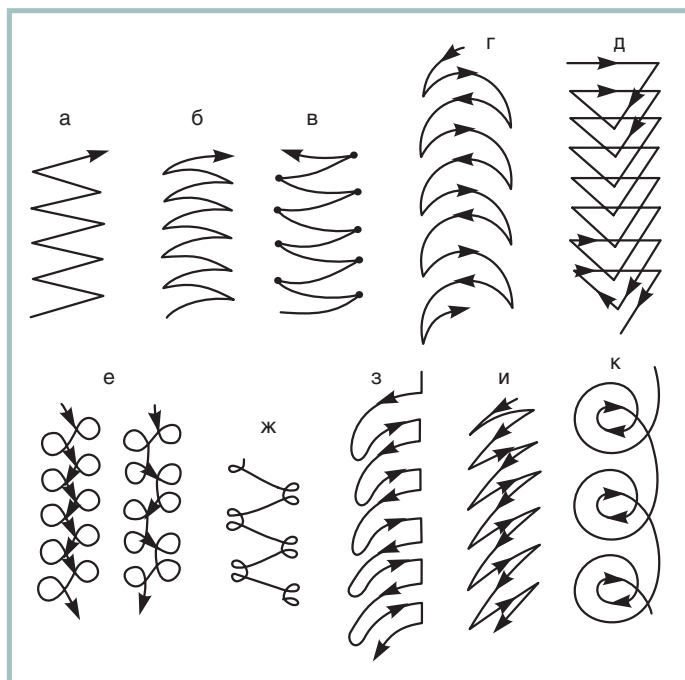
Основные виды траекторий поперечных колебаний конца электрода при ручной дуговой сварке
